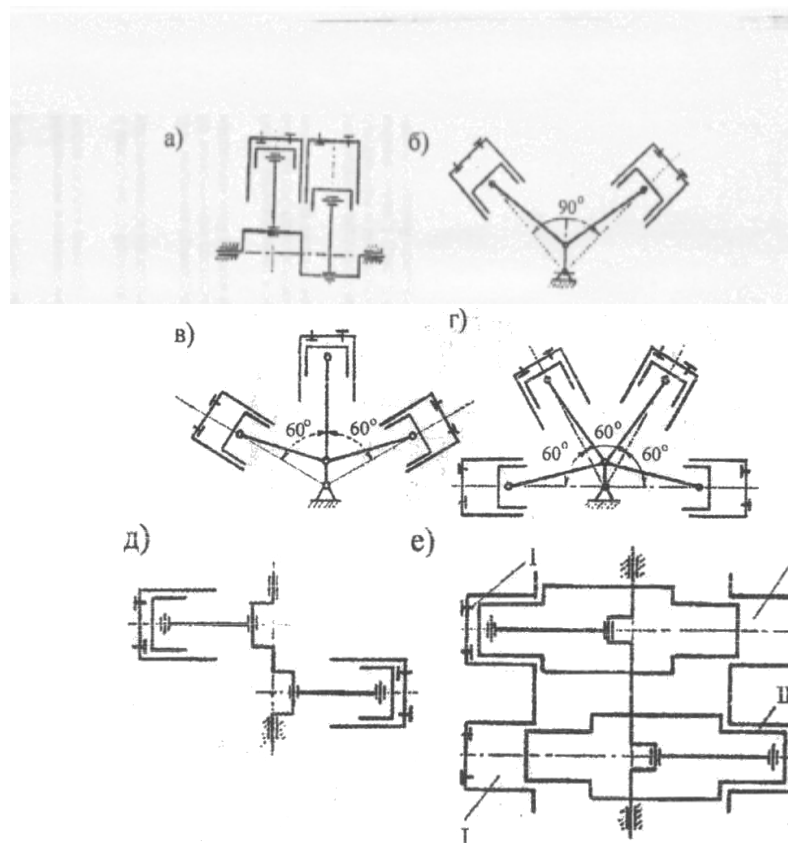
Схемы поршневых компрессоров, унифицированных по числу цилиндров: а) вертикальный с числом цилиндров 2; б) V-образный с числом цилиндров 2,4,6; в) Ш-образный с числом цилиндров 4 и 8; г) X-образный с числом цилиндров 4 и 8; д) оппозитивный с числом цилиндров 2,4,6, 8; е) оппозитивный двухрядный с числом цилиндров в первой ступени - 3, во второй ступени - 1 (I, II - порядковые номера ступеней сжатия)
